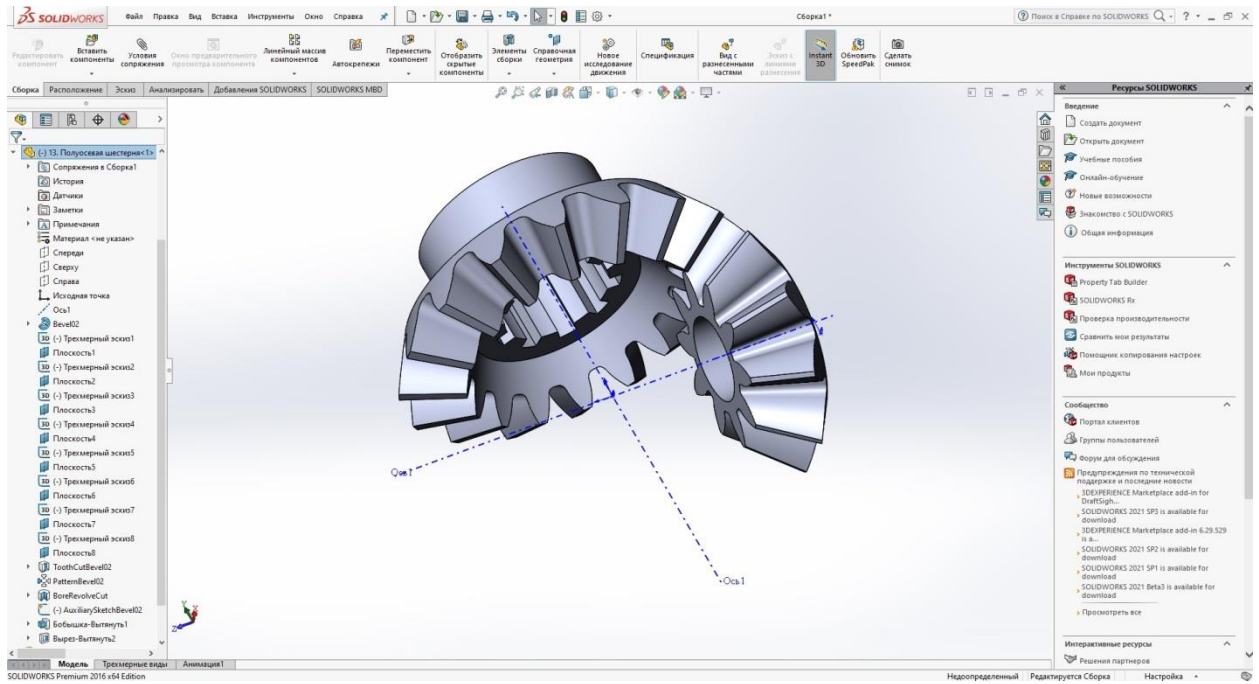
3D модель зубчатого зацепления конической передачи
